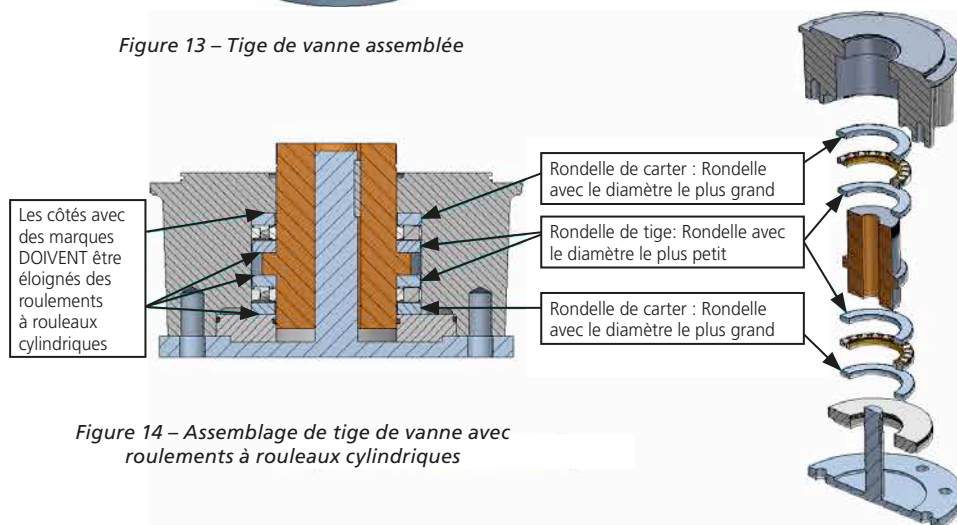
Assemblage de tige de vanne avec roulements à rouleaux cylindriques
